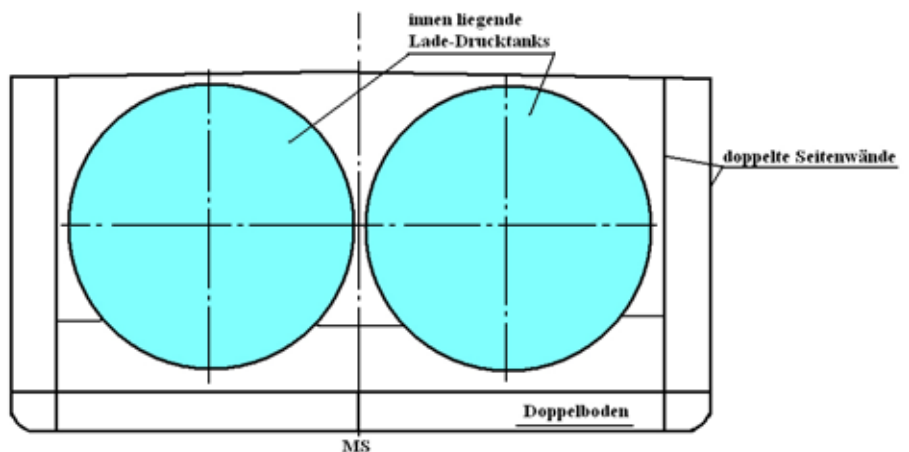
Prinzipieller Konstruktionsaufbau des Laderaumbereichs
